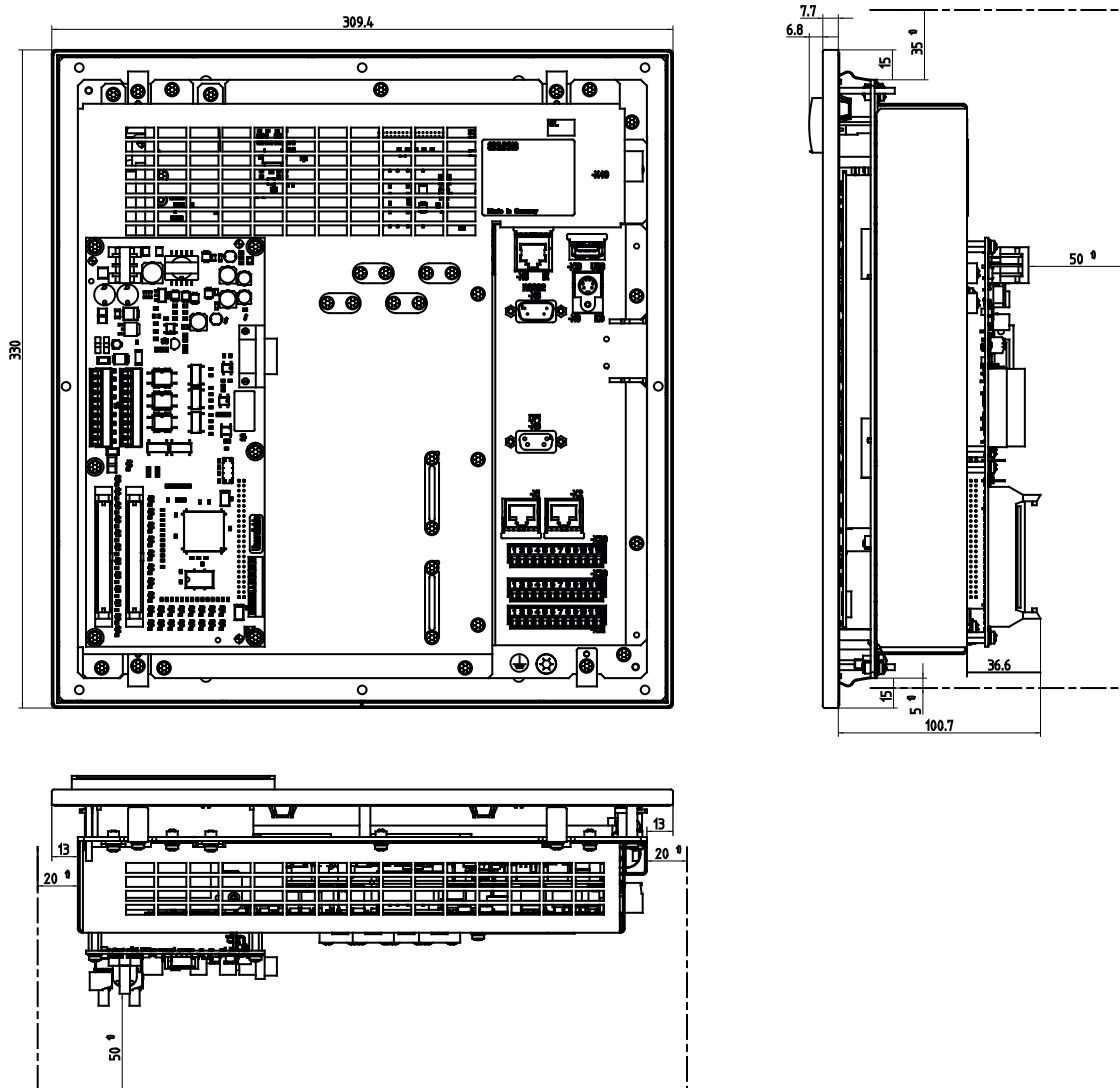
带 MCPA 模块的 CNC 操作面板的外形尺寸图
